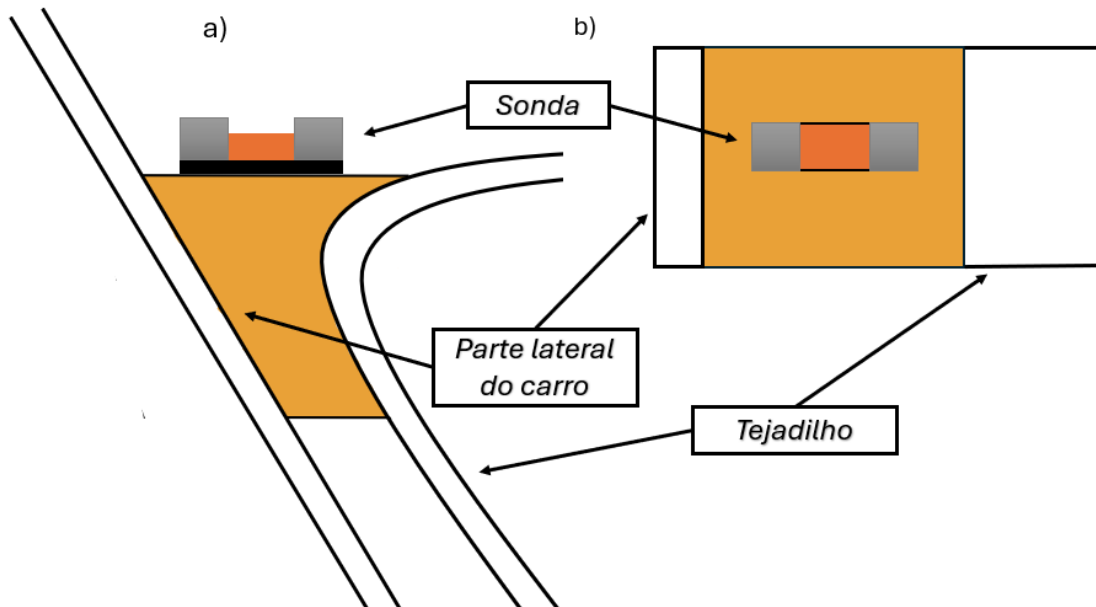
Posicionamento da bobina sob o cordão de soldadura durante o ensaio
